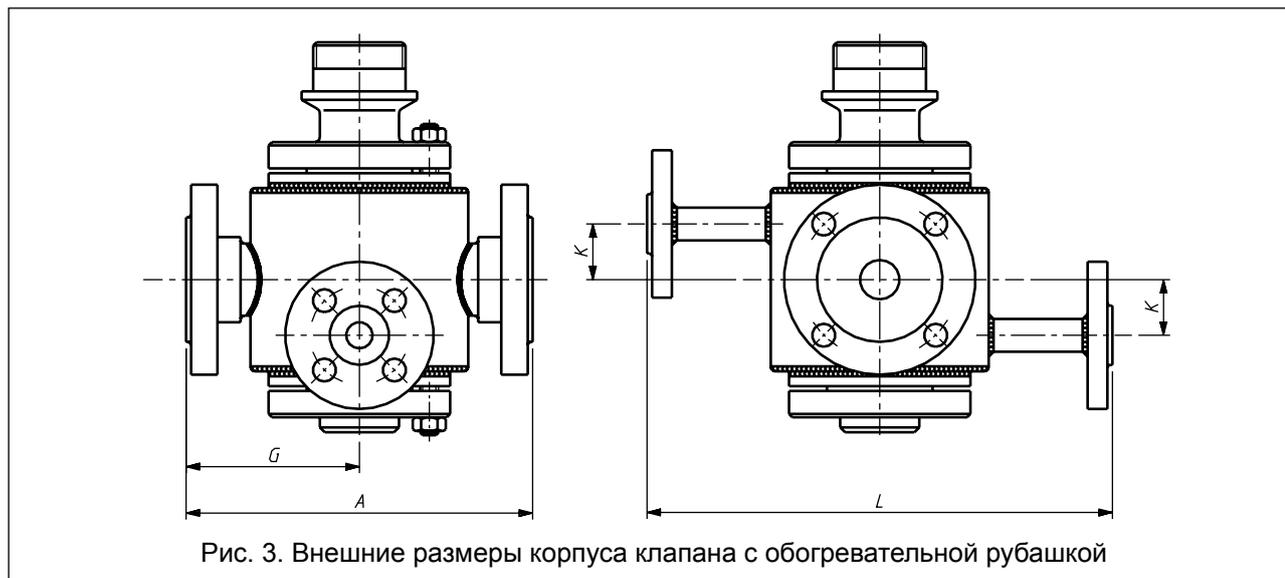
Внешние размеры корпуса клапана с обогревательной рубашкой
